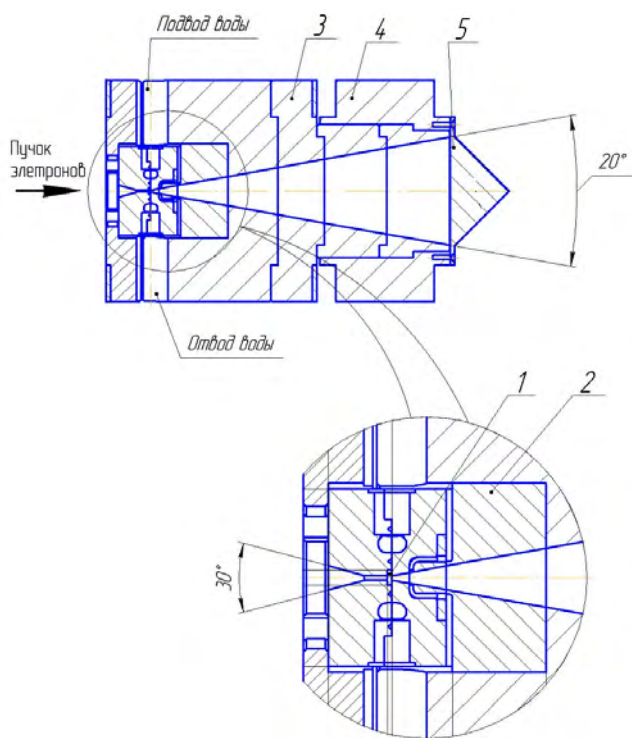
Мишень ТИ: 1 – вольфрамовый конвертер; 2 – медный коллиматор; 3 – свинцовый кожух; 4 – стальной корпус; 5 – алюминиевый фильтр
